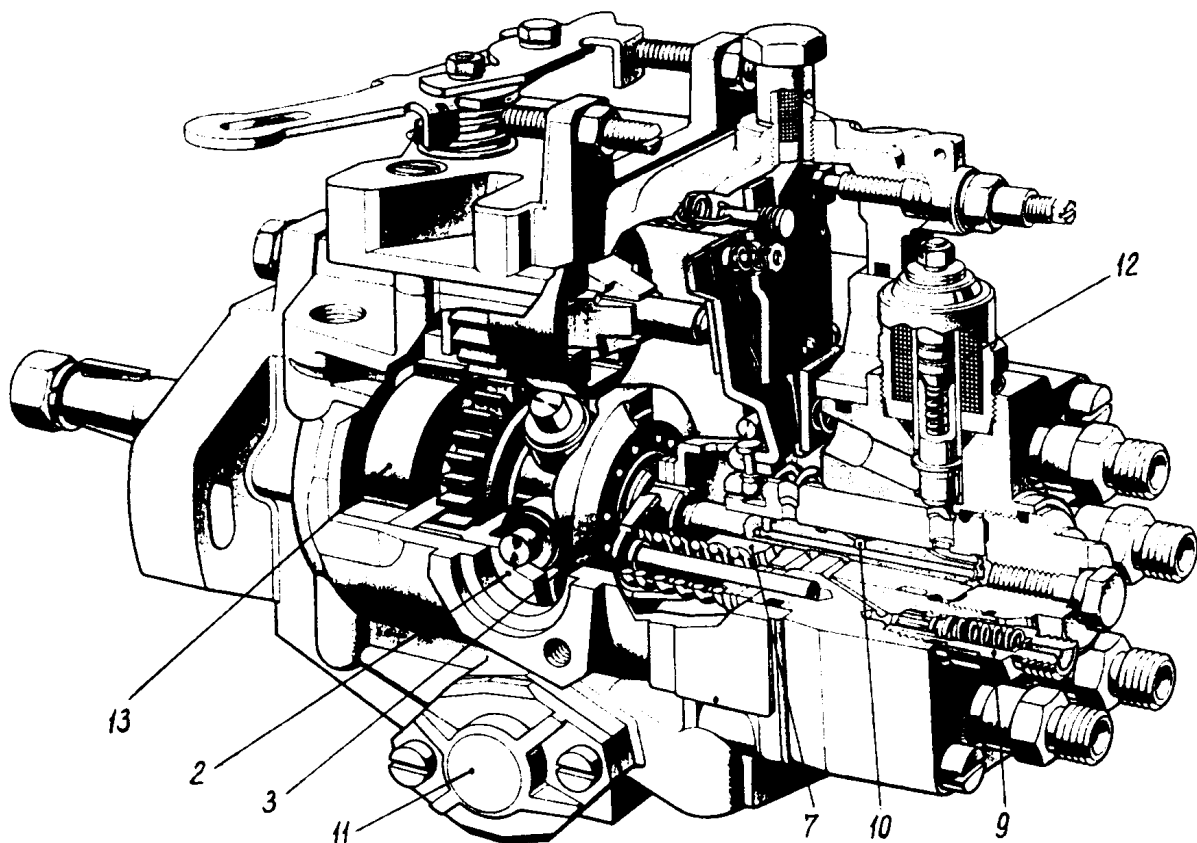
ПНВТ VE фірми "R.Bosch" базової конструкції з механічним регулятором
